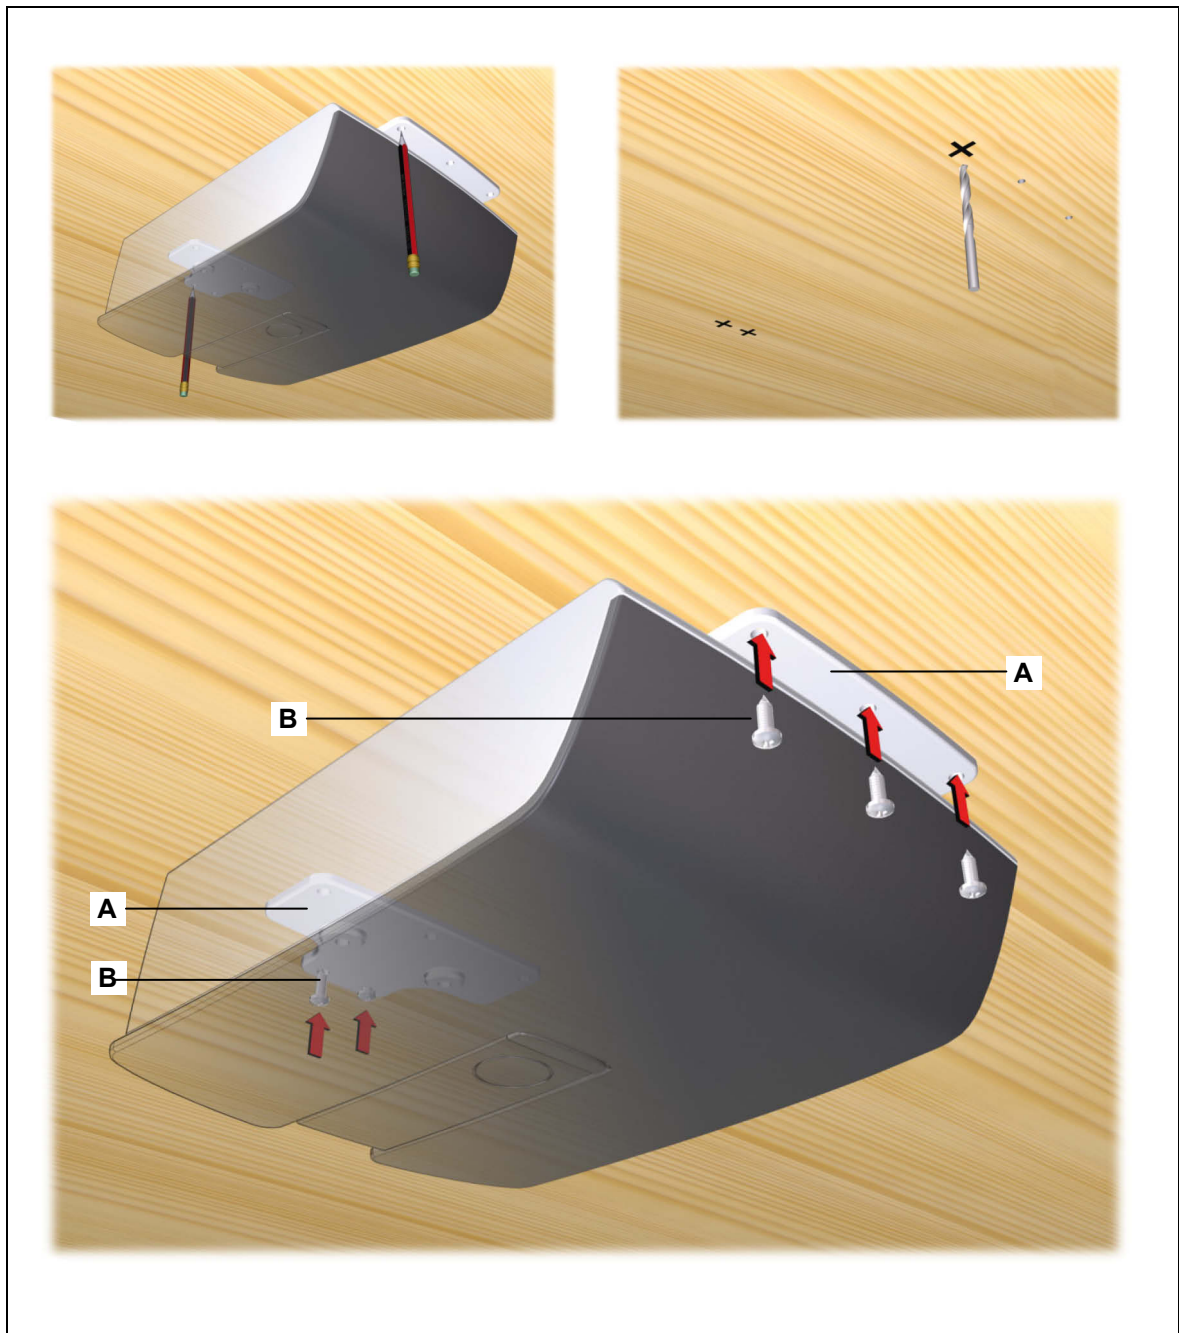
Montage des POWER SUPPLY HE-300 SMPS am Endprodukt
